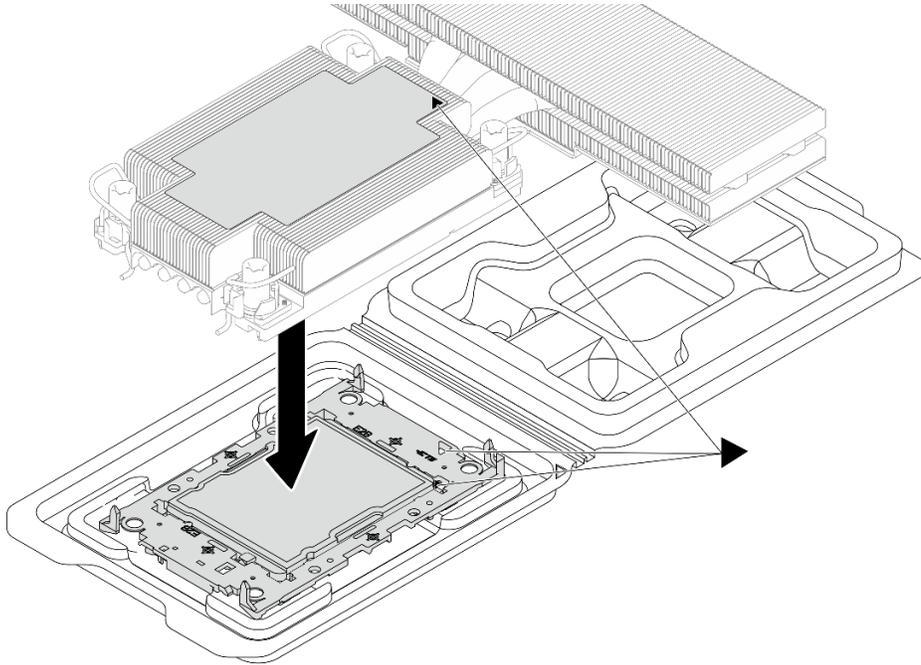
Assemblage du module de processeur-dissipateur thermique avec le processeur dans le plateau d'expédition
